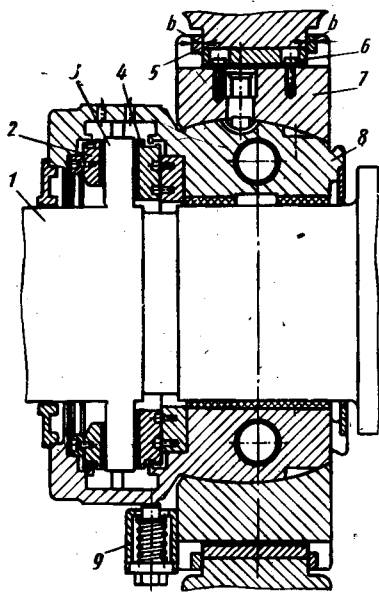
Комбинированный опорно-упорный подшипник и его установка в корпусе:
